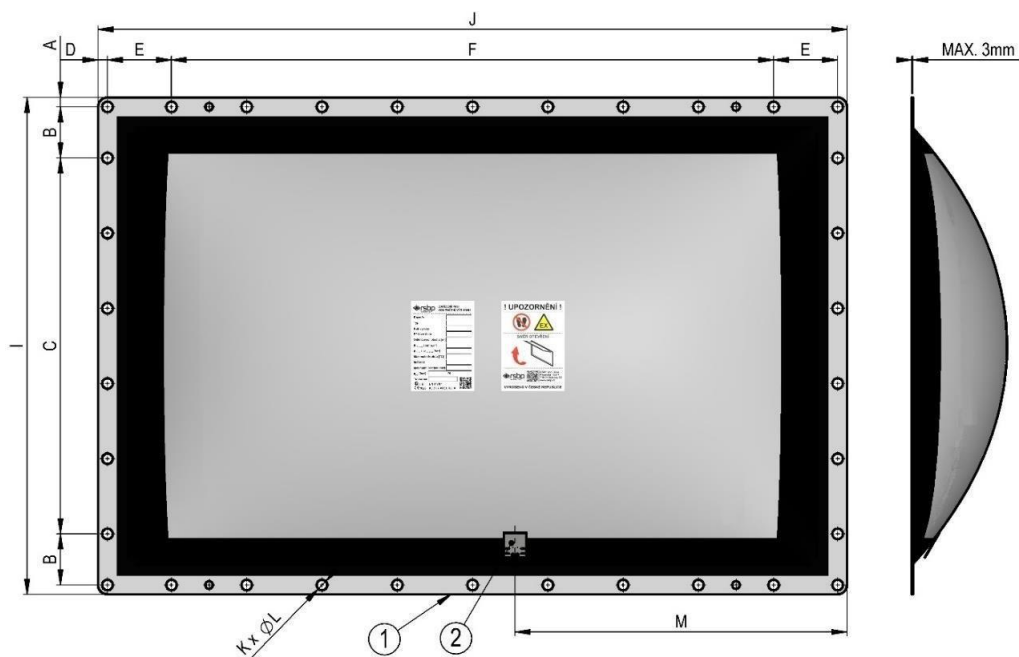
Габаритная схема для VMP тип D прямоугольного
